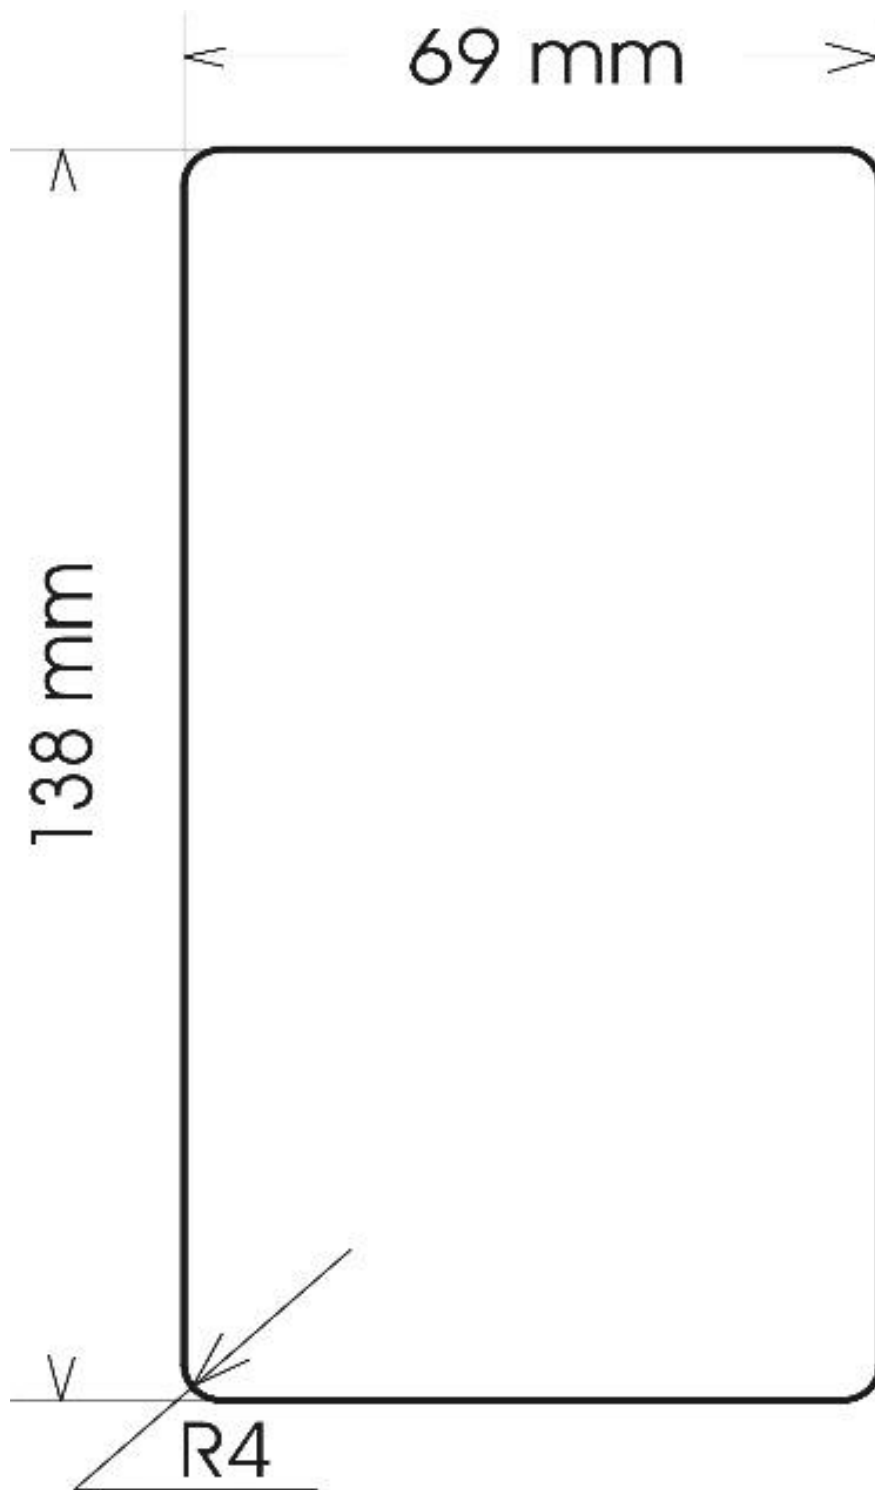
Разметка под установку блока ВК–381ЛПД в щите.
